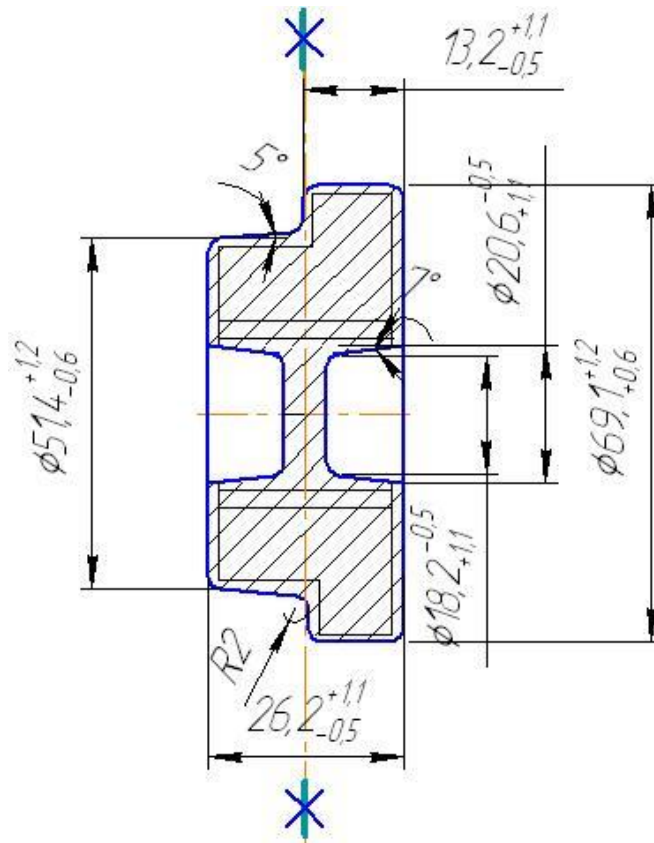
Ескіз штампованої заготовки шестірни
